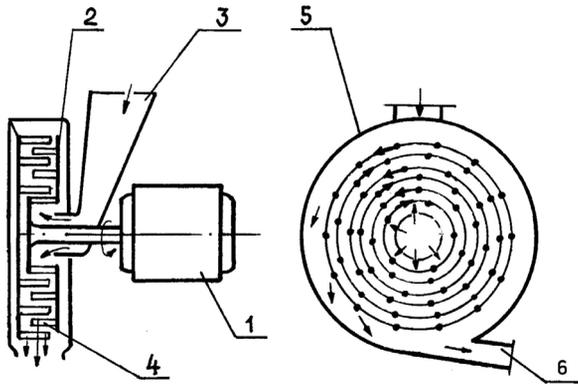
Схема дисмембратора: 1 – электродвигатель, 2 – вращающийся диск, 3 – загрузочная воронка, 4 – пальцы, 5 – корпус, 6 – патрубок для отвода суспензии.
